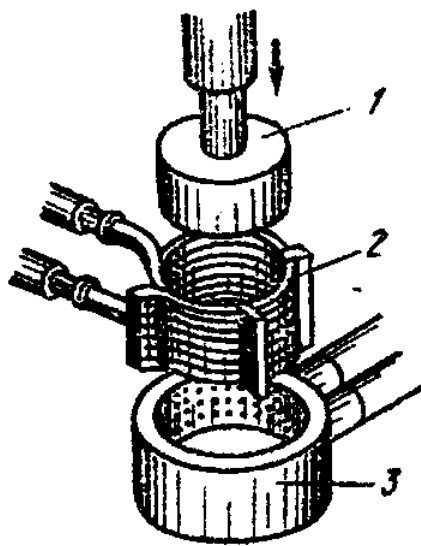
Поверхнє гартування струмами високої частоти: 1 - заготовка; 2 - індуктор; 3 - пристрій для охолодження (спрейер)
